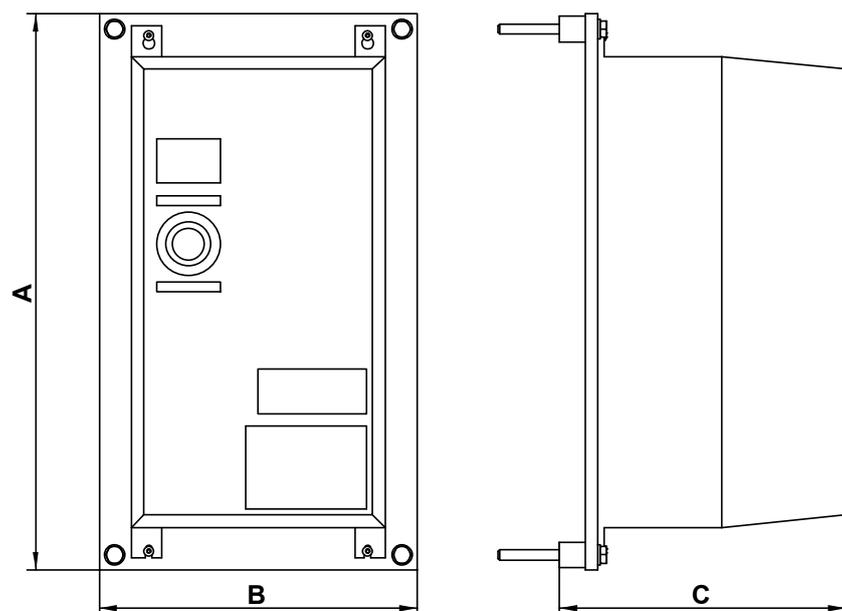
Maßzeichnung Frequenzumrichter FU-X Eco
